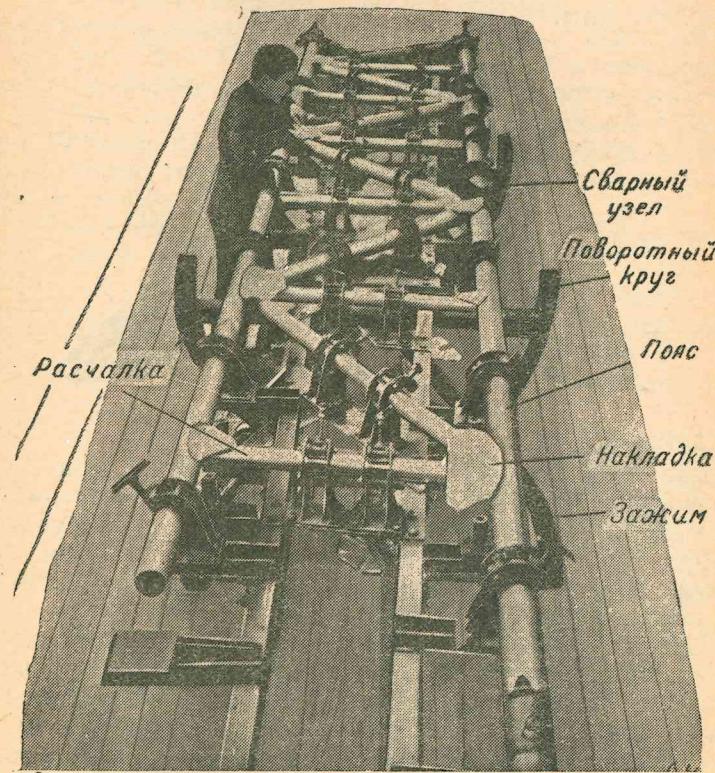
Установка расчалок трубчатого лонжерона. Цифрами 1 и 2 обозначены расчалки, соединяемые без накладок непосредственно к узлу.
